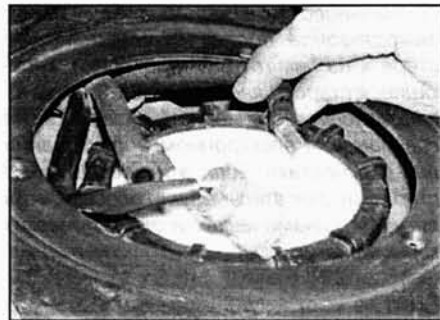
Отсоедините шланги подачи и слива топлива в бак
